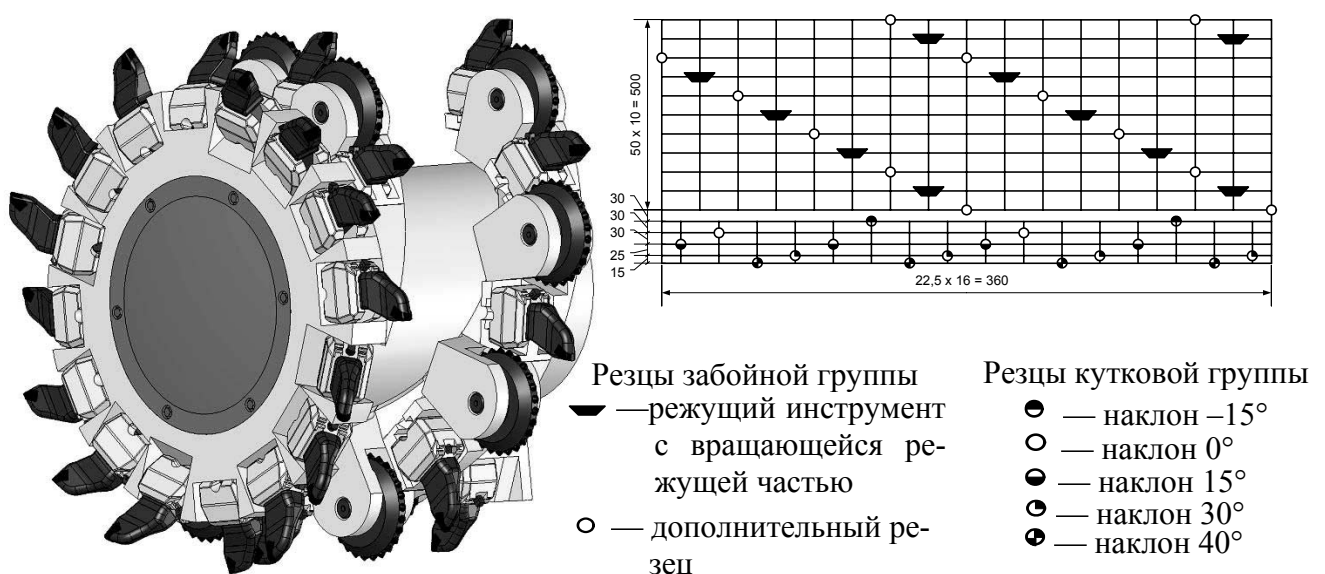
Вид исполнительного органа с комбинированной схемой набора вращающегося режущего инструмента
